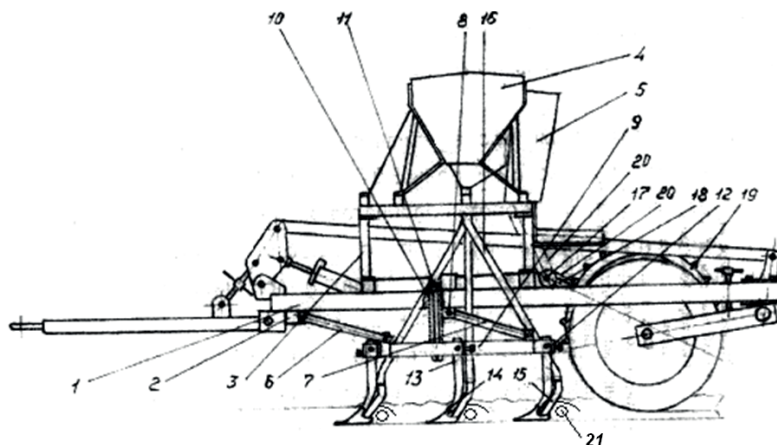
Схема сеялки-культиватора адаптерного типа
